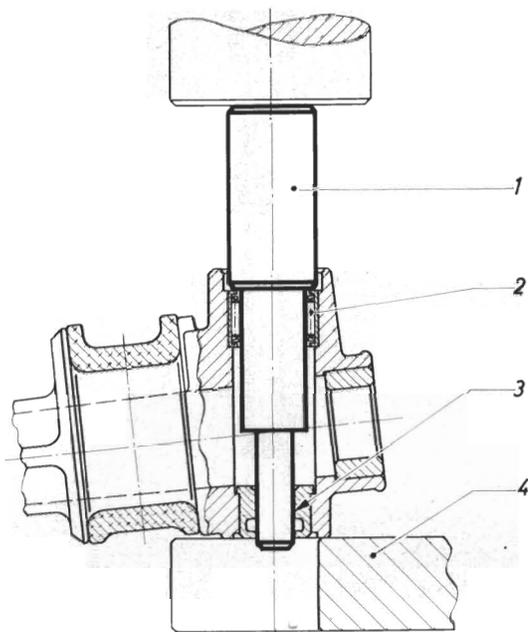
Nadellager in Lenkgehäuse eindrücken
